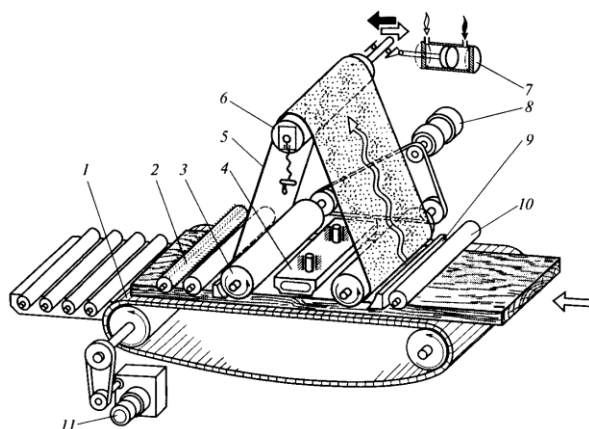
Одноагрегатний широкострічковий шліфувальний верстат з конвеєрною подачею: 1 – конвеєрний механізм подачі; 2 – щітка; 3 – барабан; 4 – утюжок; 5 – шліфувальна стрічка; 6 – ролик; 7 – пневмоциліндр; 8, 11 – електродвигуни; 9 – притиск; 10 – притискний ролик
